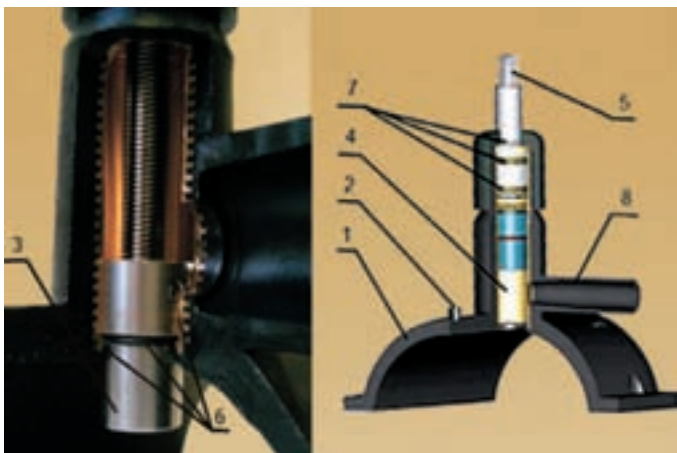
Конструкция вентиля для врезки под давлением Frialen, тип DAV: 1) корпус из полиэтилена ПЭ 100; 2) контакты для сварки; 3) интегрированная фреза с верхним и нижним упорами; 4) металлическая гильза для хода фрезы; 5) вращающийся шпindel на 14 мм из легированной стали 1.4305 для управления приводом фрезы; 6) трехкратное внутреннее уплотнение в нижнем положении (ПЭ-металл, уплотнительное кольцо, металл–металл); 7) трехкратное внешнее уплотнение (уплотнительное кольцо); 8) выходной патрубков, рассчитанный на две сварки.
